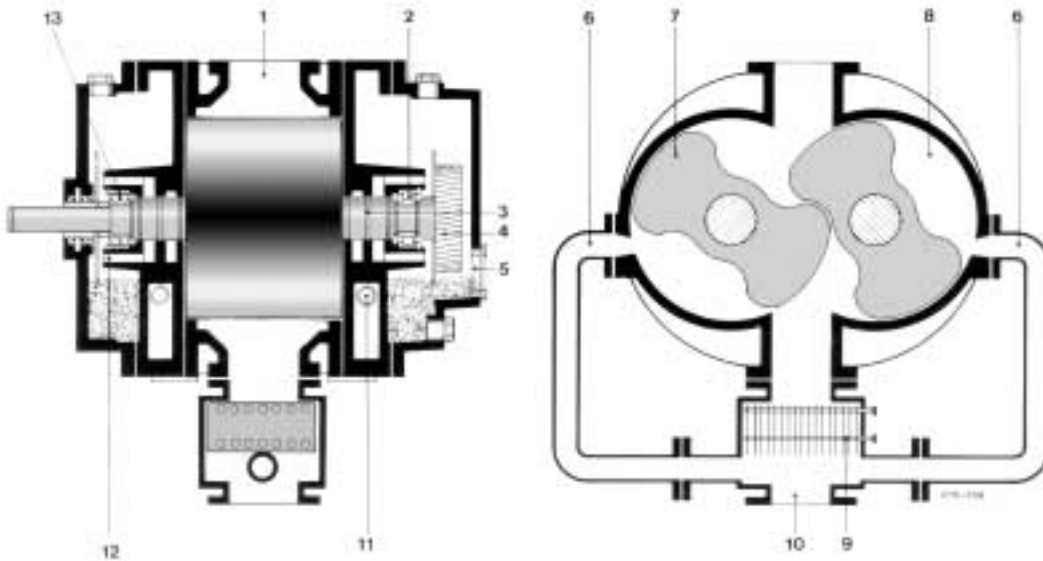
Schnittdarstellung einer gasumlaufgekühlten Wälzkolbenvakuumpumpe WGK (Pfeiffer Vacuum GmbH).
